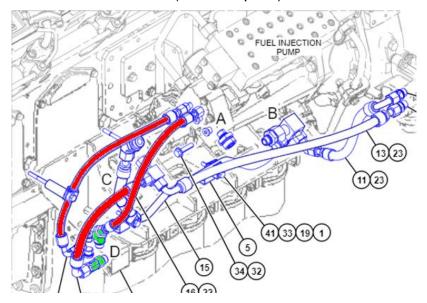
Partes a ser retiradas y partes para reutilizar (vista manual de partes)
